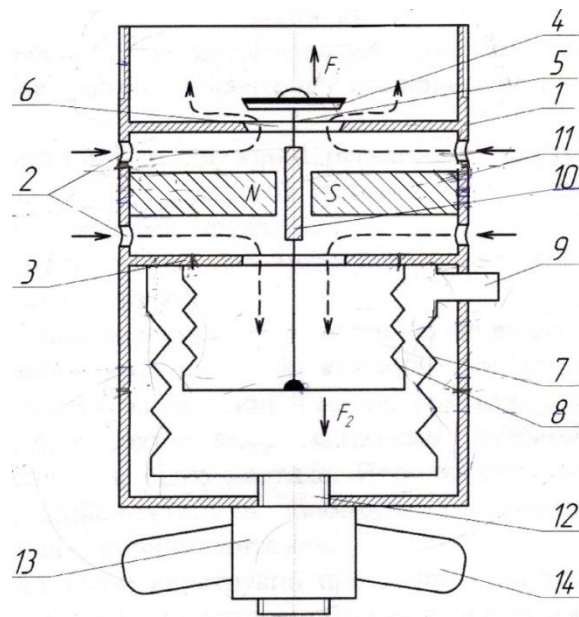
Схема розробленого регулятора вакууму доїльної установки: 1 – корпус; 2 – бокові отвори; 3 – перемичка; 4 – клапанний механізм з клапаном; 5 – шток; 6 – сідло; 7, 8 – зовнішній та внутрішній сильфони; 9 – патрубок; 10 – пластини; 11 – постійні магніти; 12 – гвинт; 13 – гайка; 14 – рукоятка
